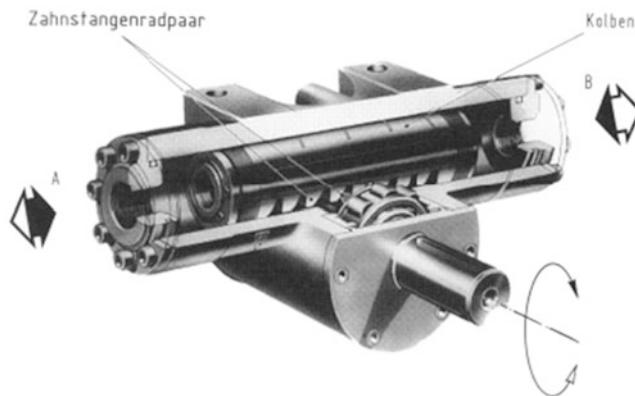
Zahnstangenschwenkmotor, Einkolbenmotor in Standardausführung (ST, Pleiger)
